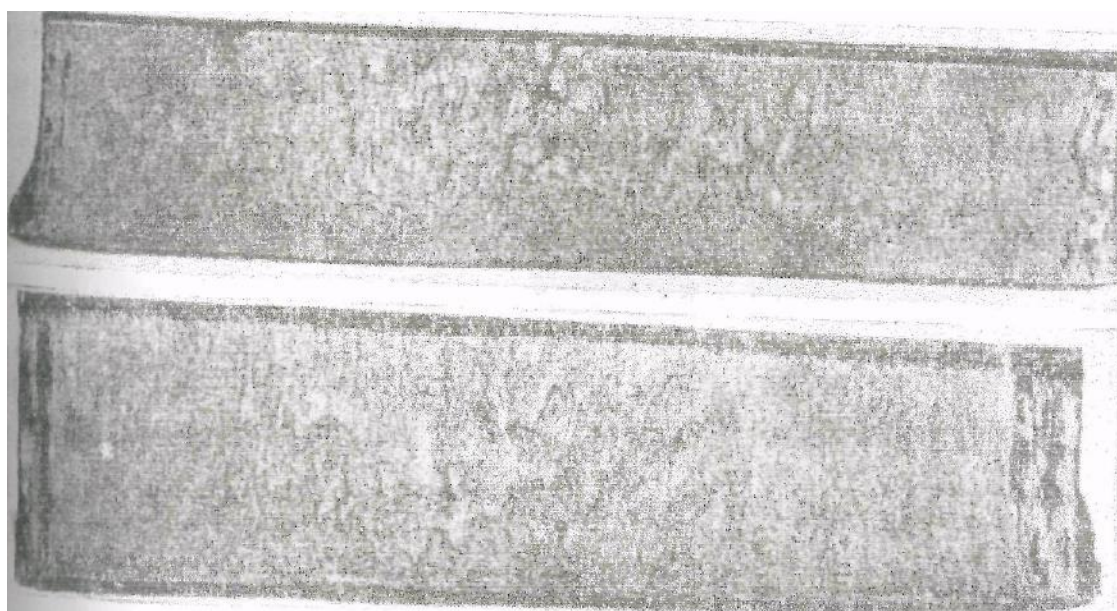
Злами шайб від заготовок з поверхневими рванина. «Підшкірні» бульбашки.
